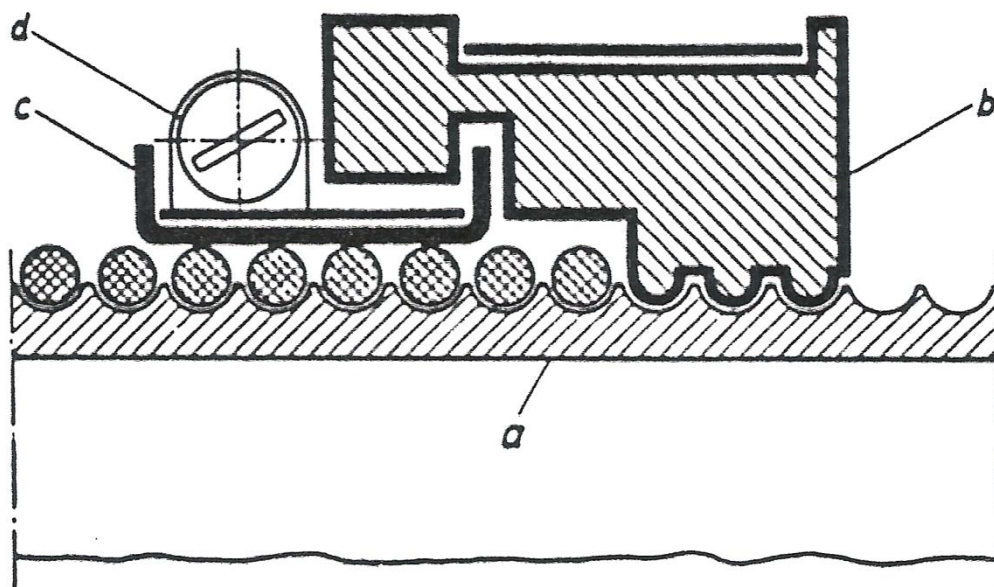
Enrollador de cable. a- tambor de cable, b- tuerca de guiado, c- anillo que se aplica sobre las espiras enrolladas, d- resorte.(1)
